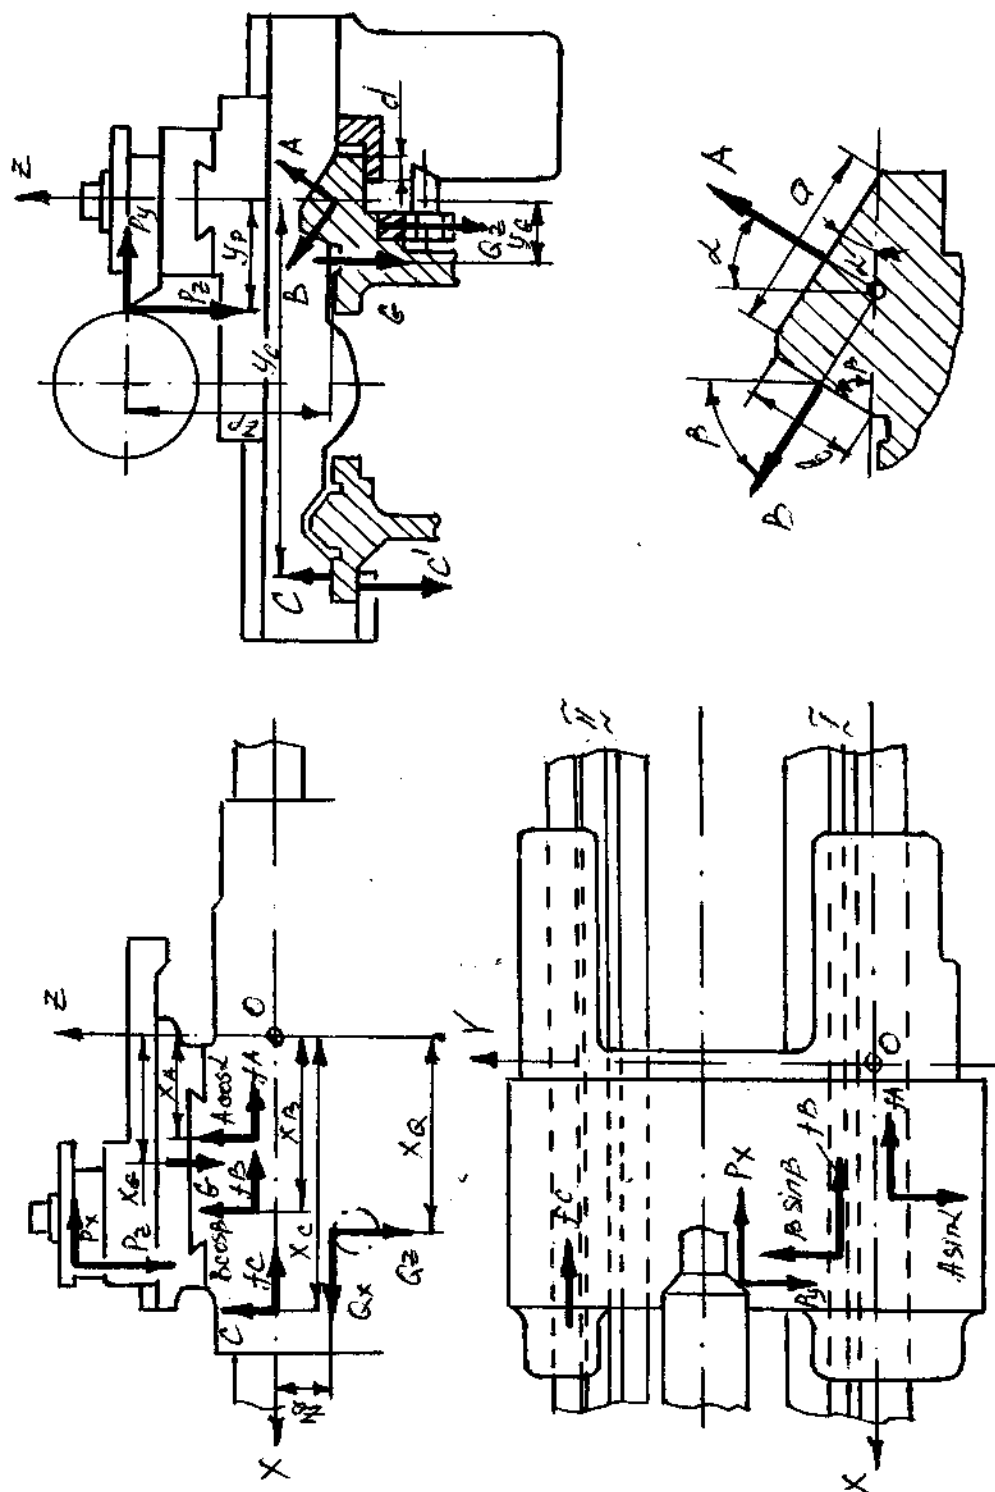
Схема для розрахунку сил, що діють в направляючих супорта.
